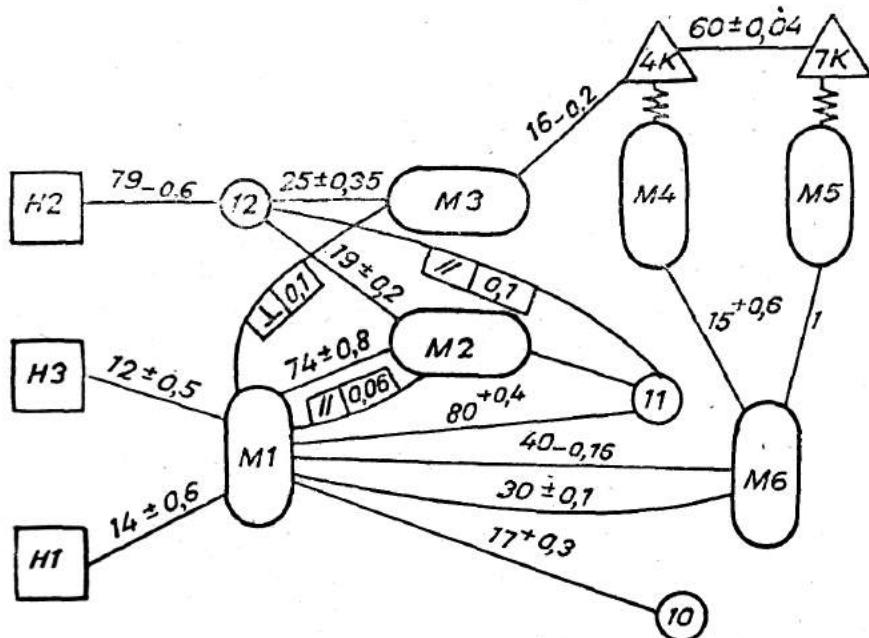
Зв'язки між поверхнями та модулями поверхонь поворотної опори.
